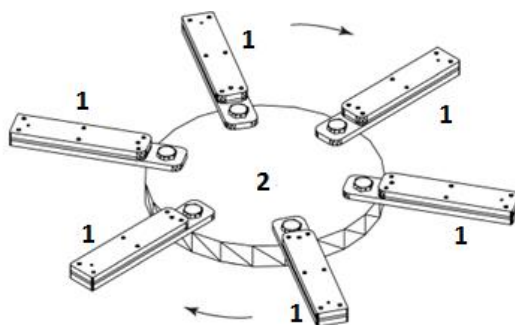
Dispositivo de moldação rotacional, adaptado de [17]
